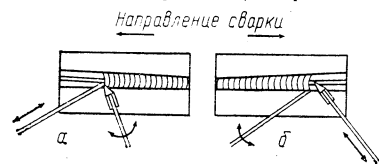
Техника газовой сварки: а — левая сварка; б — правая сварка
